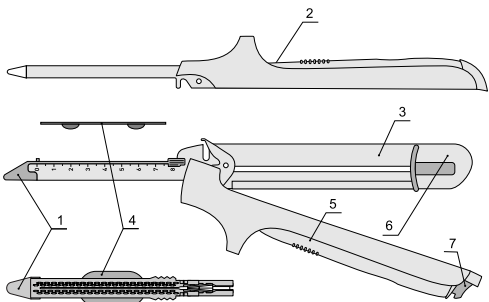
Внешний вид линейного сшивающе-режущего аппарата Volkman: 1 - сменная кассета; 2 - ответная часть корпуса; 3 - кассетная часть корпуса; 4 - предохранитель кассеты; 5 - ручка правого корпуса; 6 - ползунок ножа; 7 - кнопка открытия браншей.
